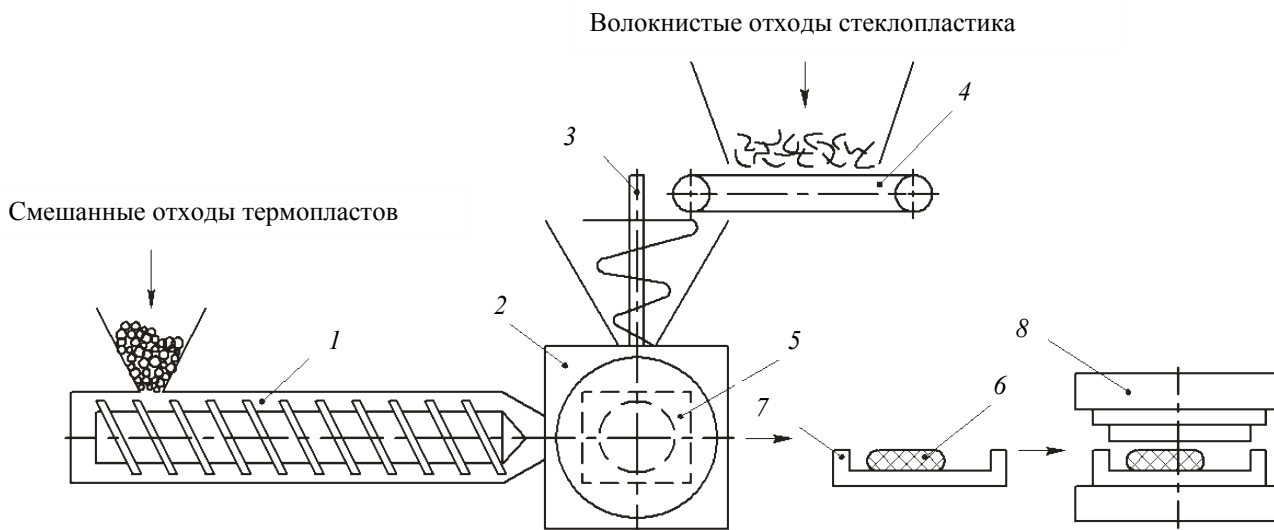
Схема компаундирования: 1 – червячный пластикатор; 2 – дисковый экструдер-смеситель; 3 – дозатор; 4 – транспортер; 5 – накопитель; 6 – заготовка; 7 – пресс-форма; 8 – гидравлический пресс
